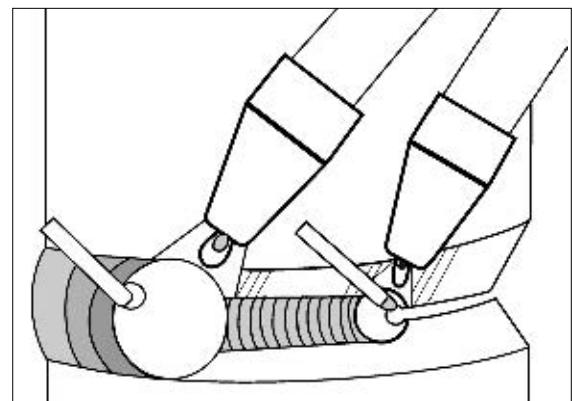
Предотвращение выливания жидкого металла в зазор при газоэлектрической сварке
